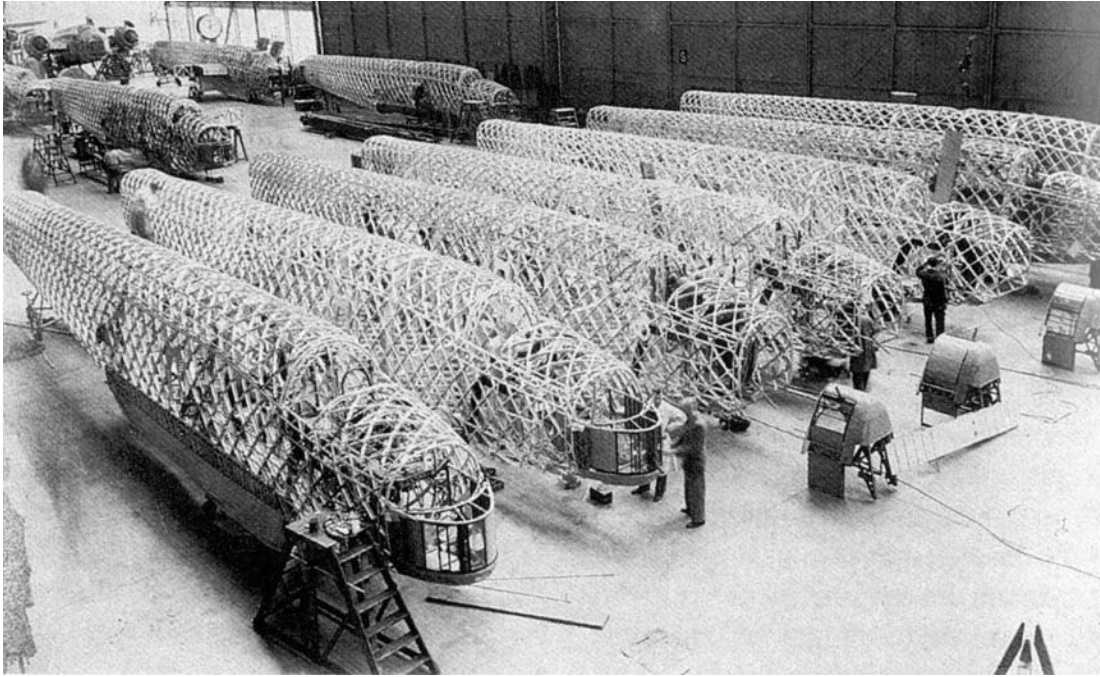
Planta de fabricación de fuselajes del bombardero Wellington.
